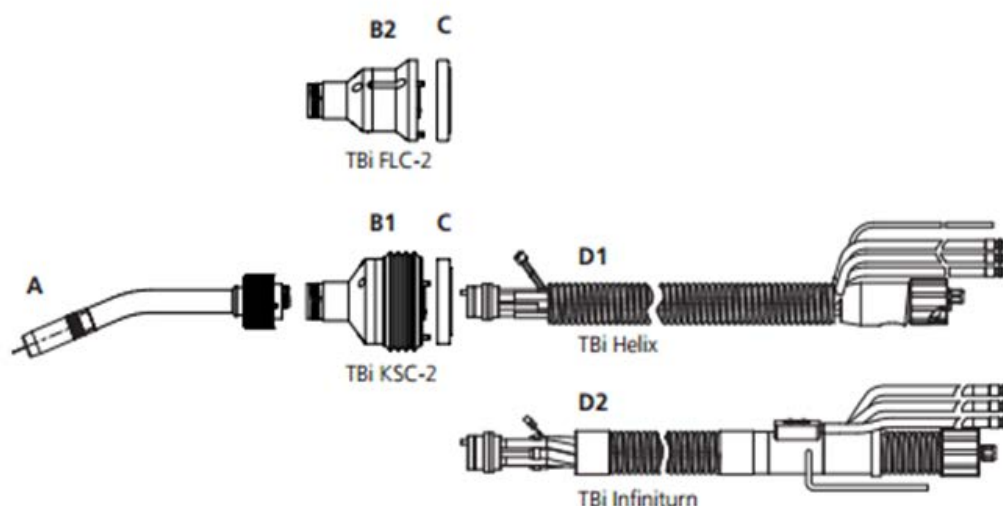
Варианты подключения сварочной горелки
